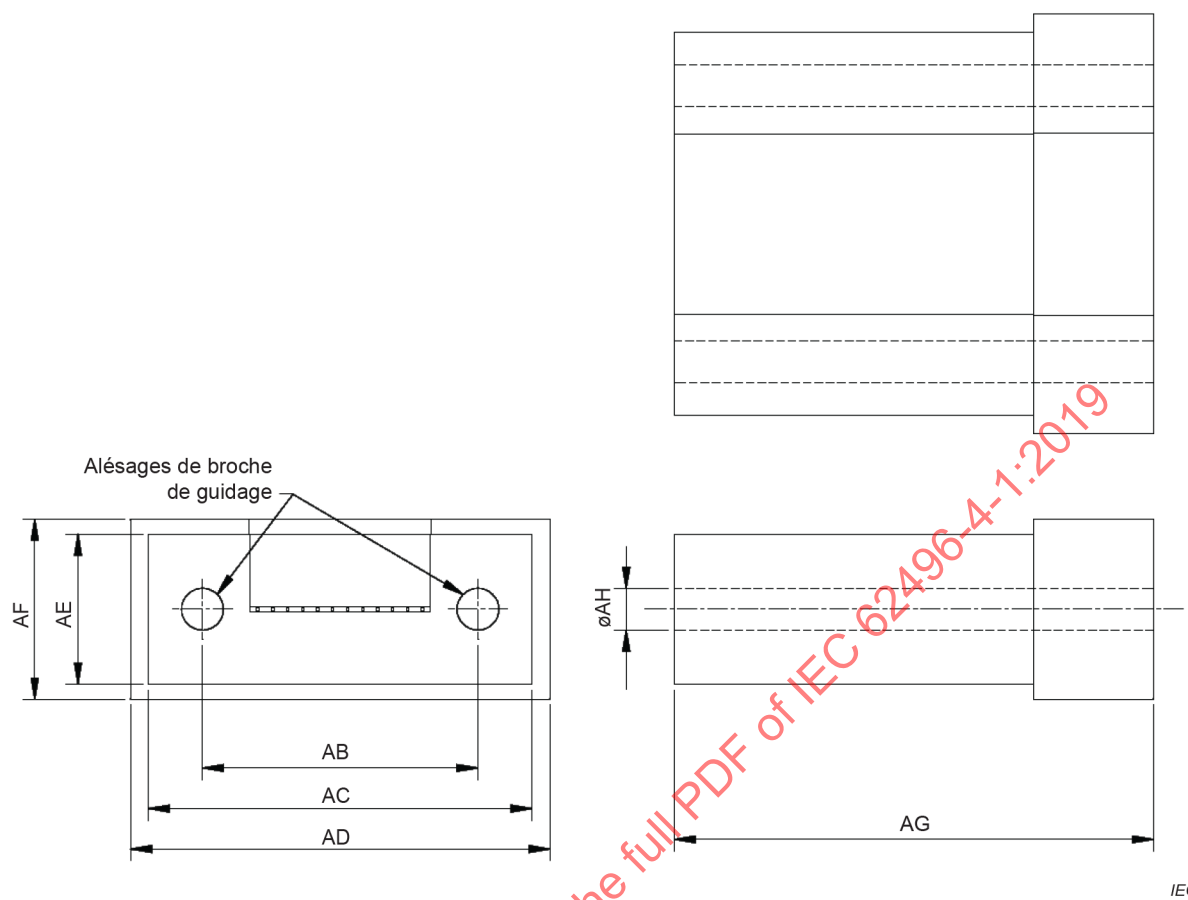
Dimensions d'interface de douze cœurs pour l'ensemble
